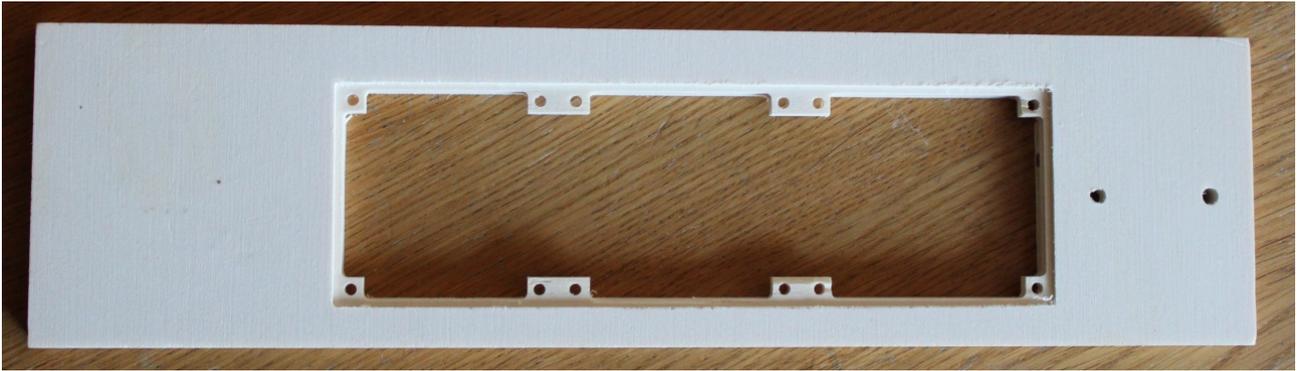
Grundplatte mit den Ausfräsungen für die Platinen.
